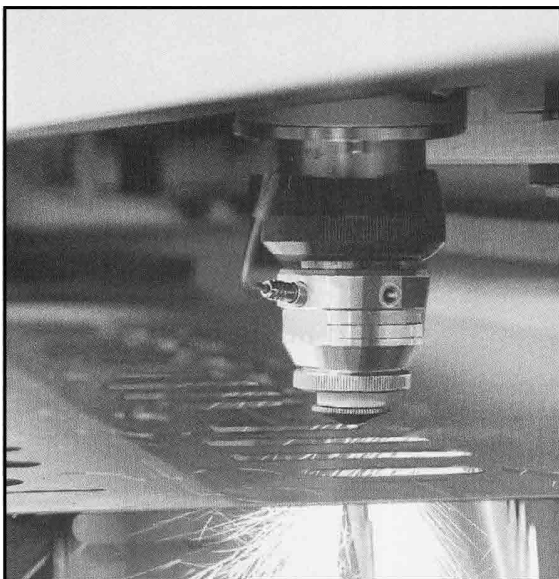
Робоча зона установки для лазерного різання моделі Laser-Jet
